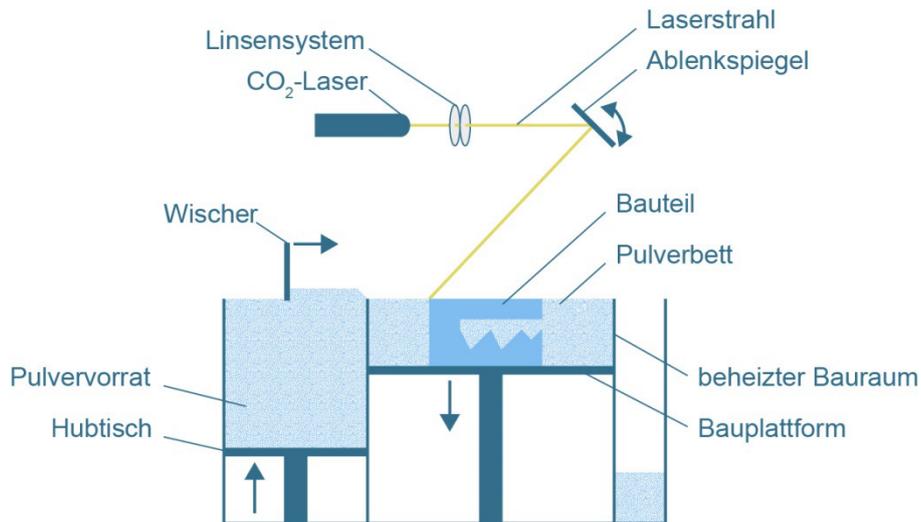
Aufbau und Elemente einer Laser-Strahlschmelzanlage
